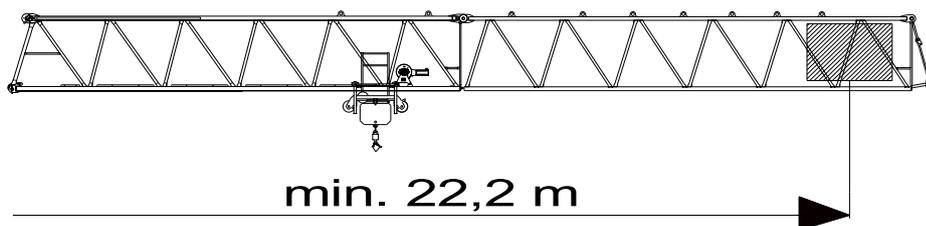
Position der Windfläche für Ausleger L1 = 23 m
